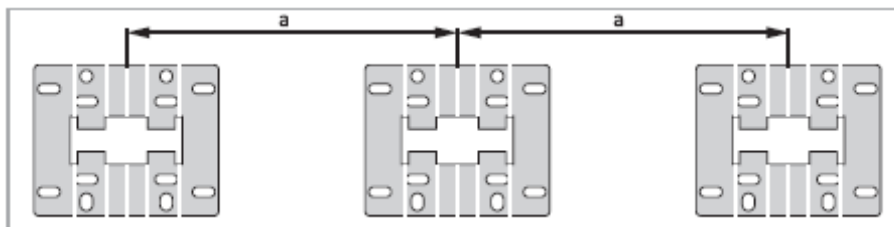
Монтаж на стене корпуса настенного монтажа
